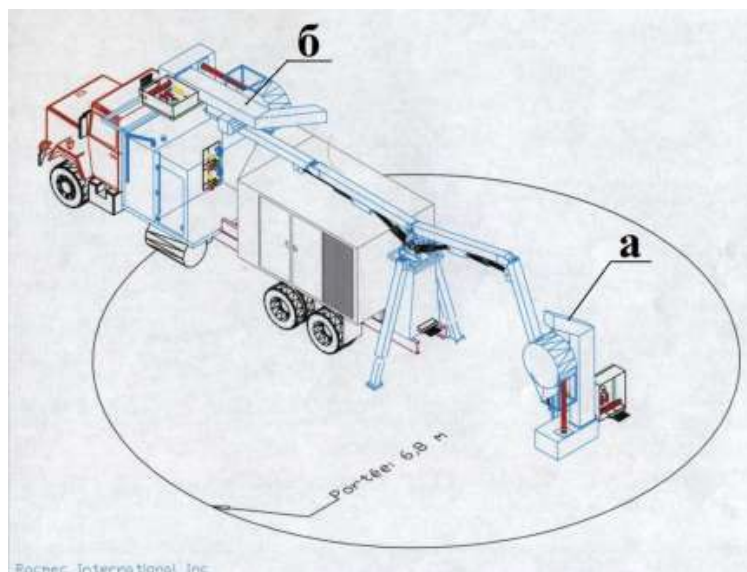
Схема расположения навесного оборудования станка термического расширения взрывных скважин «DRAGON» на трехосной платформе: а – в рабочем положении; б – в транспортном положении
